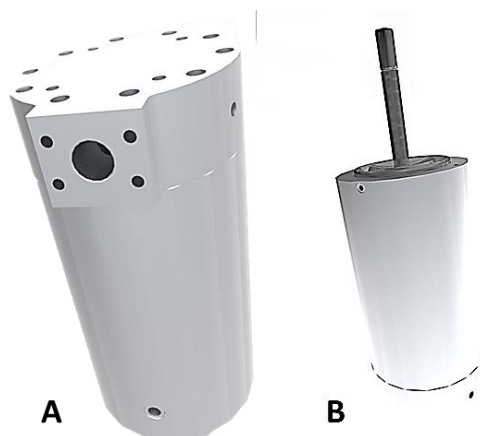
A- Cilindro hidráulico utilizado na quinadora PA13530. B- Cilindro hidráulico invertido [73].
